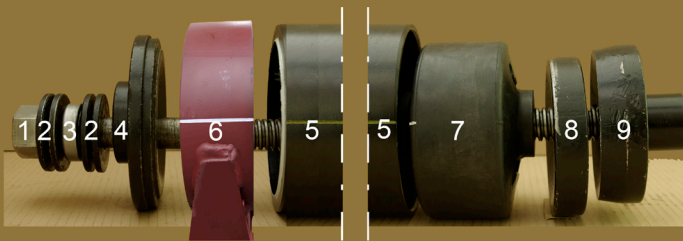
· Übersicht Montagewerkzeug (verzerrte Darstellung zur besseren Veranschaulichung)
